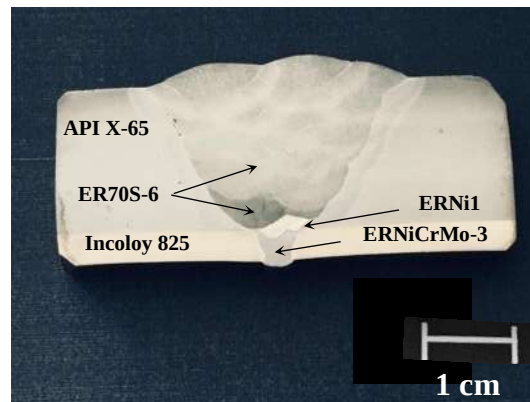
Macrografía de la soldadura de acero API X-65 revestido con Incoloy 825.
